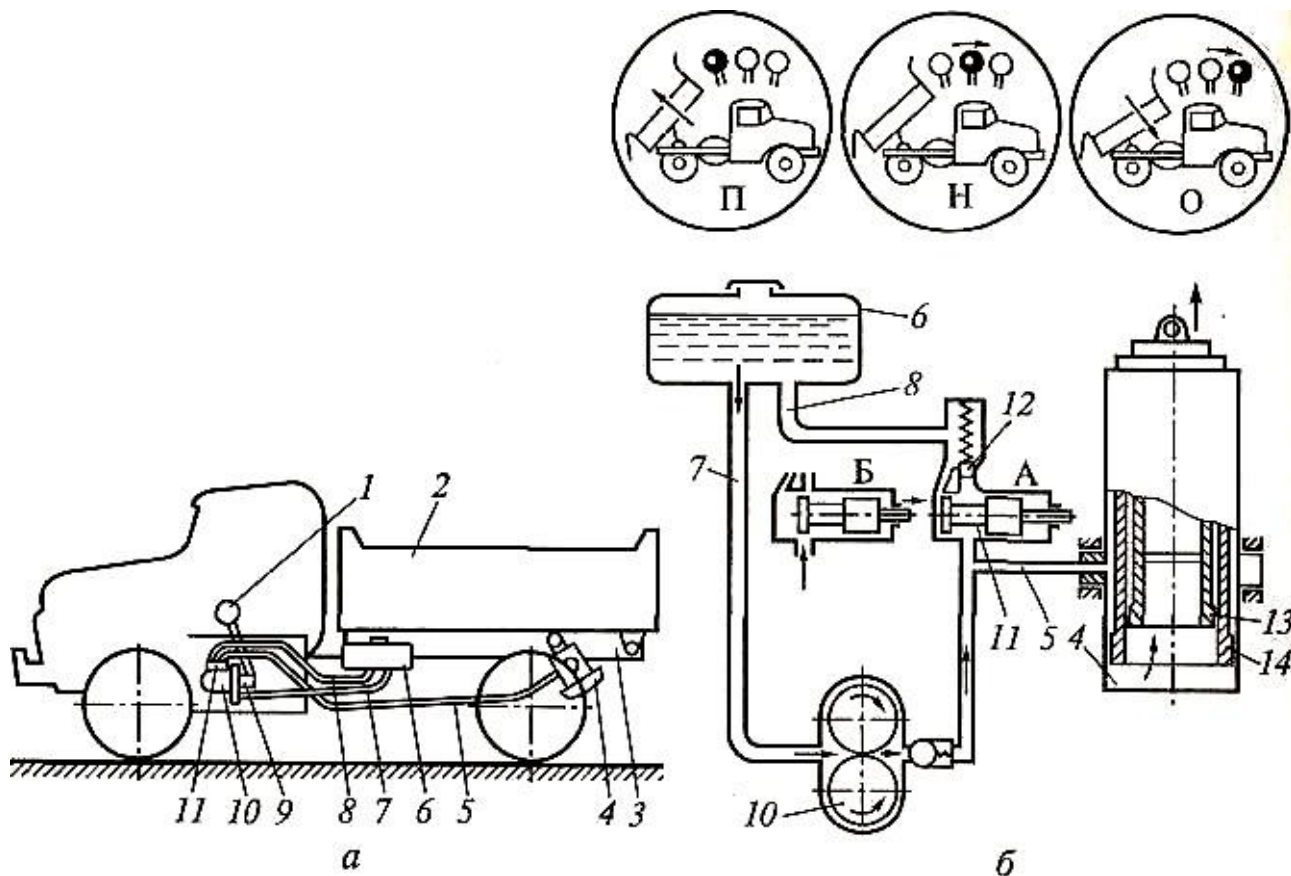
Гидравлический подъемный механизм автосамосвала ЗИЛ:
